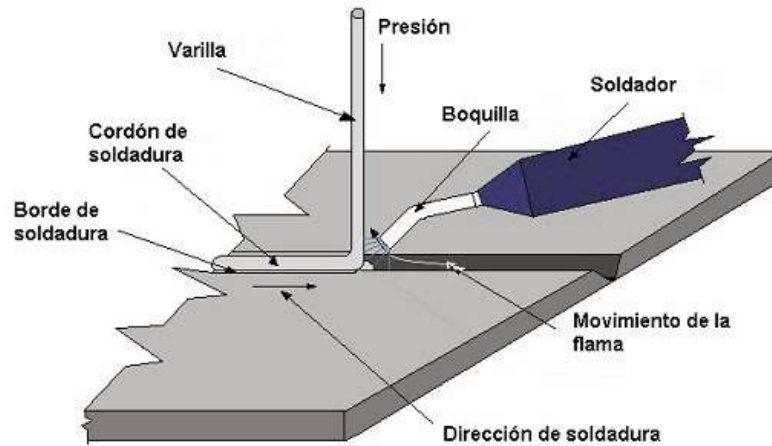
Esquema de soldadura por aire caliente (Tecnología de los Plásticos, 2013)
